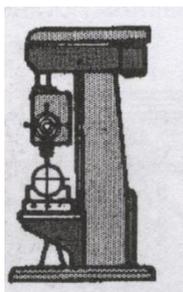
Внешний вид сверлильного (зенкерального, развёртывательного) станка
